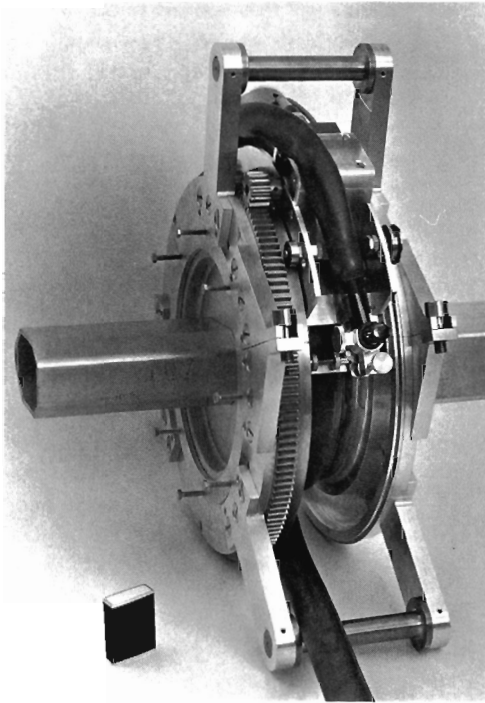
Automatische Umlaufschweißmaschine für Membran-Federungskörper (24340/20)
